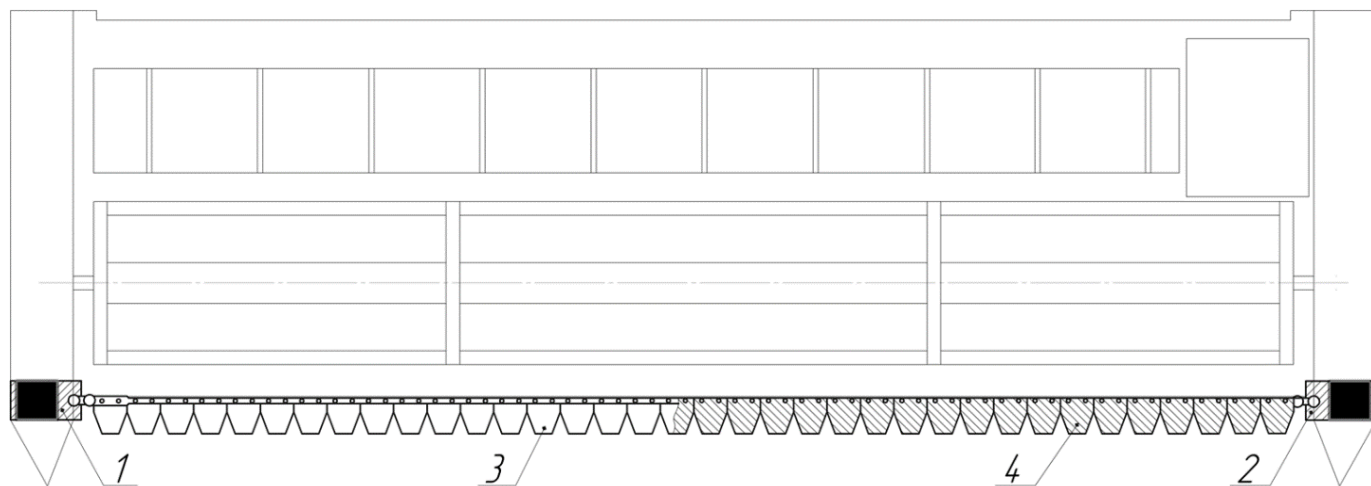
Жатка з фронтальним розташуванням приводних ДПЛАД: 1 – ДПЛАД, який приводить у дію верхню ножову смугу; 2 – ДПЛАД, що забезпечує рух нижньої ножової смуги; 3 – верхня ножова смуга ріжучого апарата; 4 – нижня ножова смуга ріжучого апарата.
